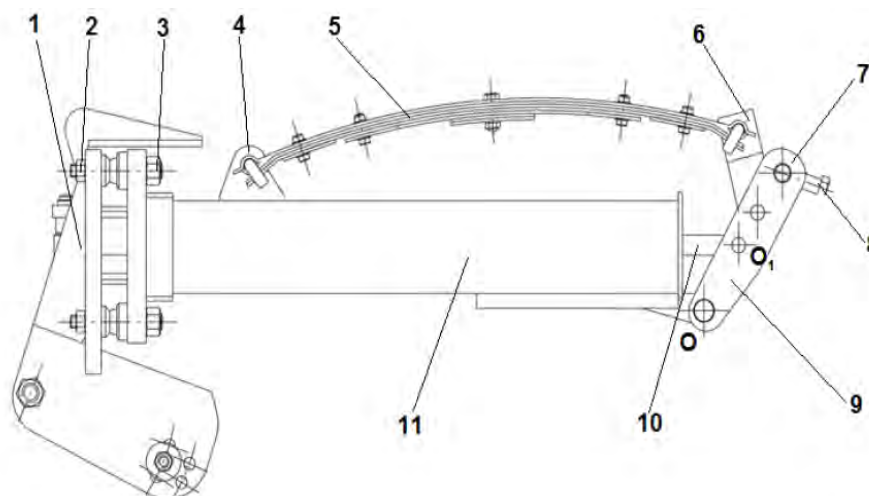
Конструкция предохранительного механизма плужного корпуса рессорного типа:
